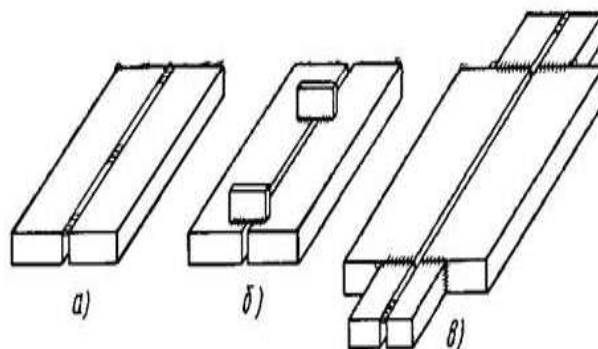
Способы закрепления деталей перед сваркой.
